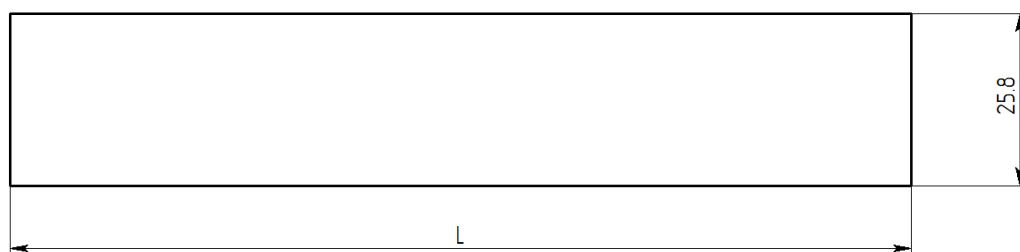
Эскиз раскроя ленты для изучаемой конструкции штампа.
